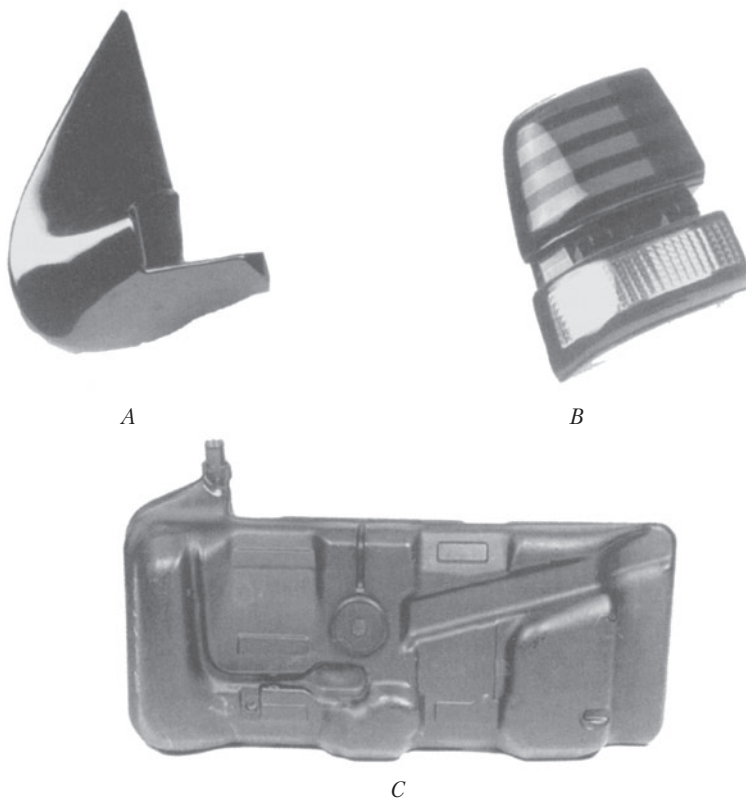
Примеры деталей многокомпонентных автомобильных систем: (А) корпус зеркала, полученный совместным литьем под давлением (ПБТ–ПК–АБС); (В) крышка заднего фонаря (ПК–ПММА); (С) соэкструдированный многослойный топливный бак (ПЭВД–малеинизированный ЛПЭНД–сополимер этилена и винилового спирта)
